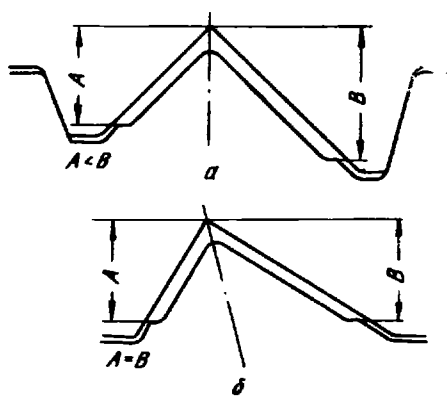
Расположение калибров на валках для прокатки угловой стали
